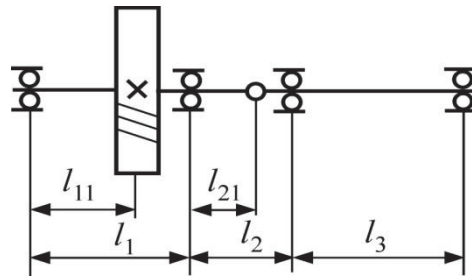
Расчетная схема четырехопорного вала с шарниром
